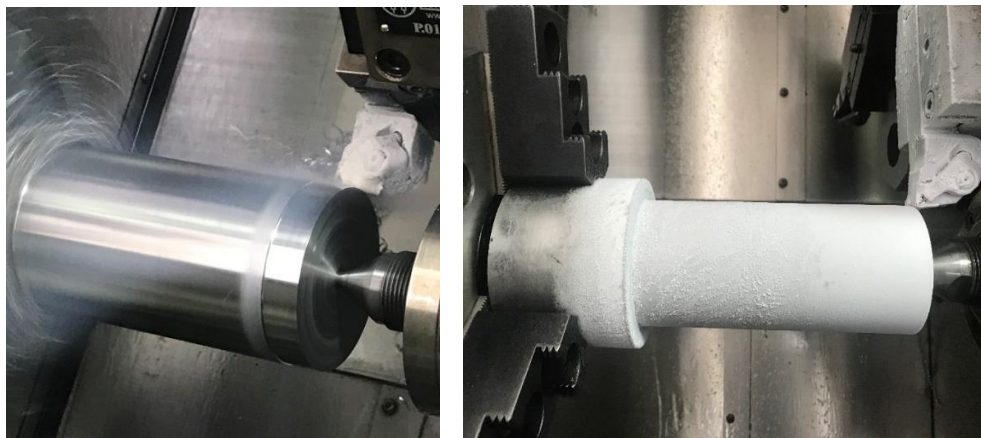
Usinagem criogênica (a) no início do processo de usinagem e (b) após o fim da usinagem e parada da máquina para a realização das medições de temperatura e acabamento superficial.
